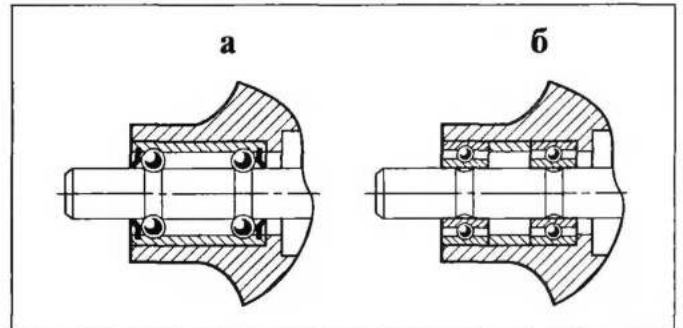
Пример некавалифицированного ремонта подшипника насоса:
